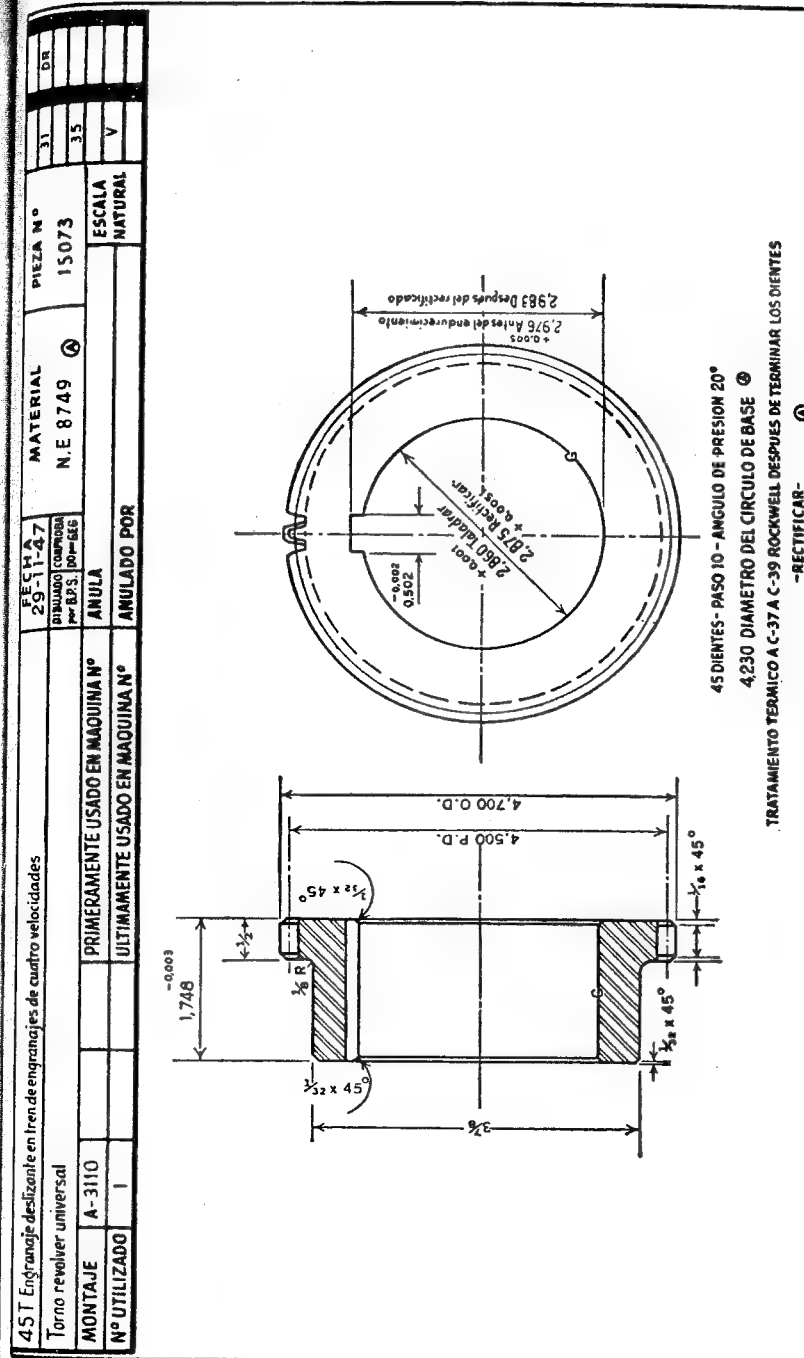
Dibujo detallado de engranaje deslizante, pieza núm. 15073.
